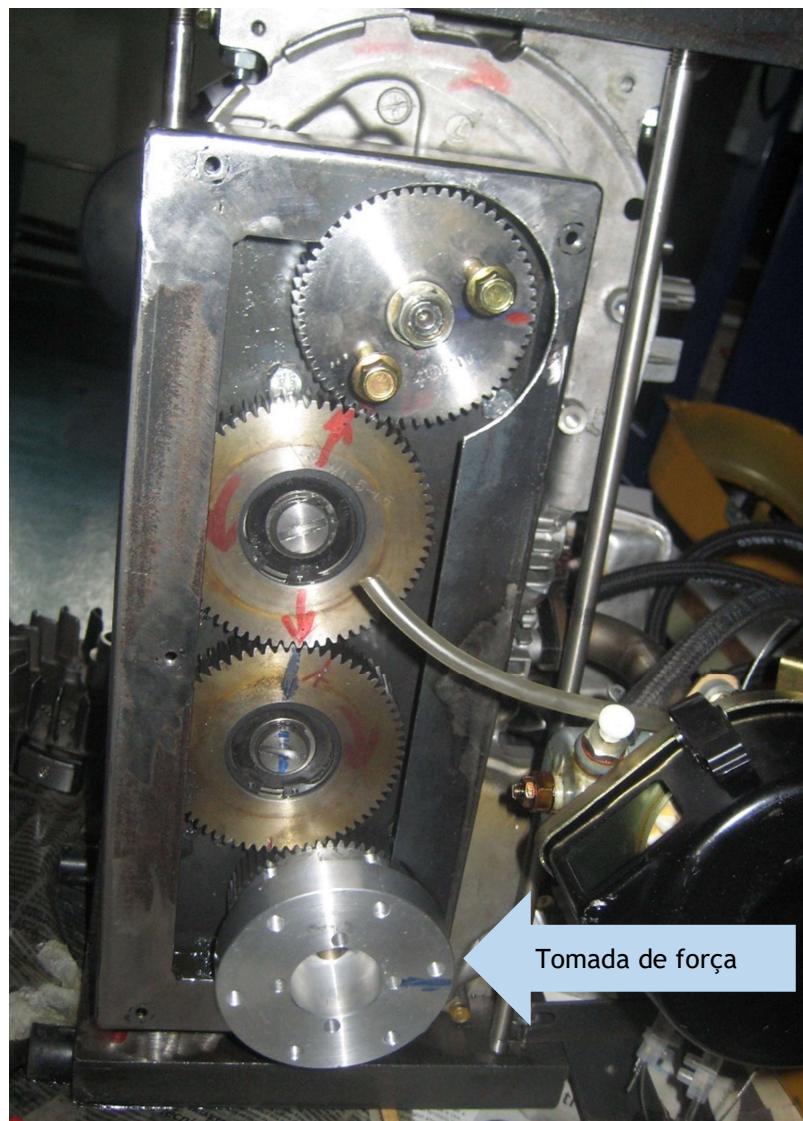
Pormenor de montagem da flange da tomada de força sobre a roda dentada.
